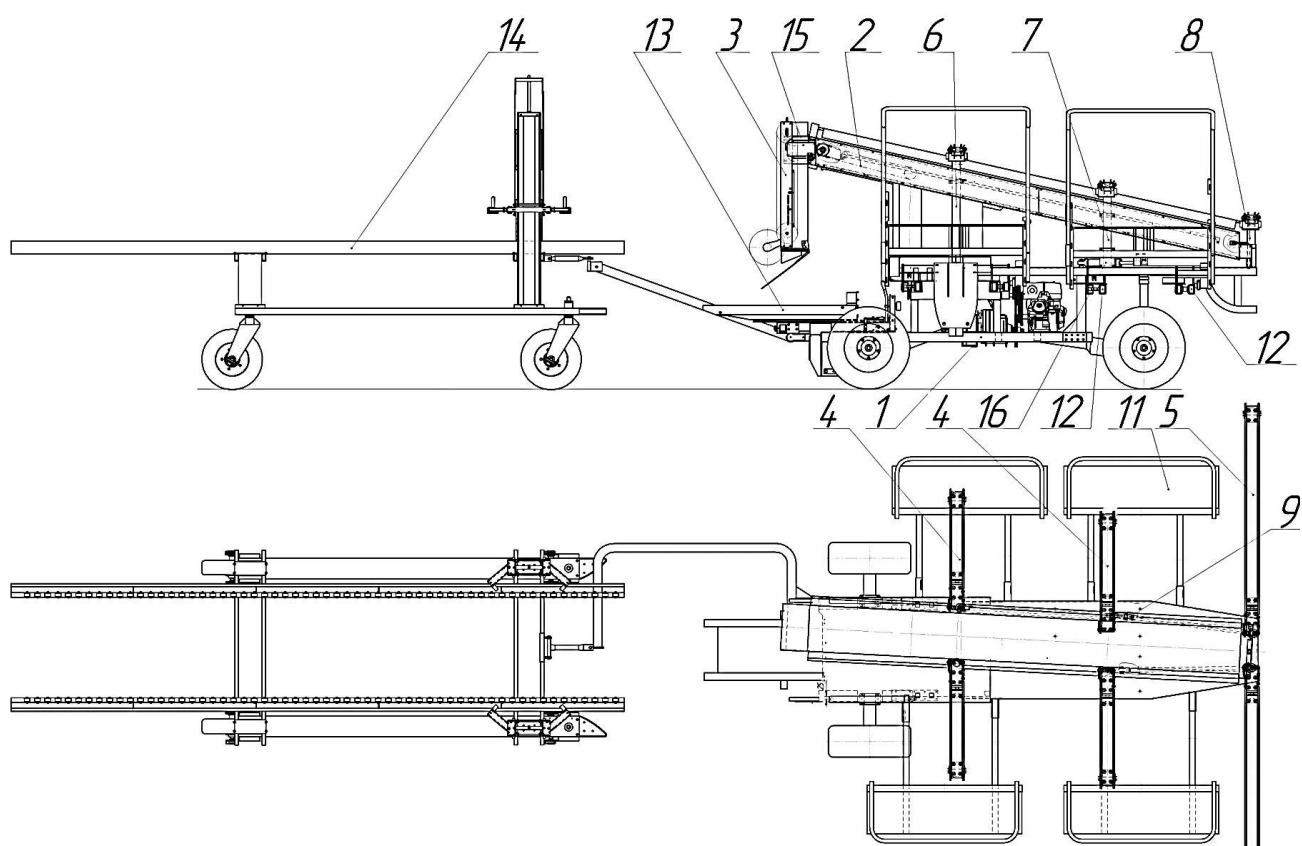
Агрегат самоходный универсальный с поточным контейнеровозом
